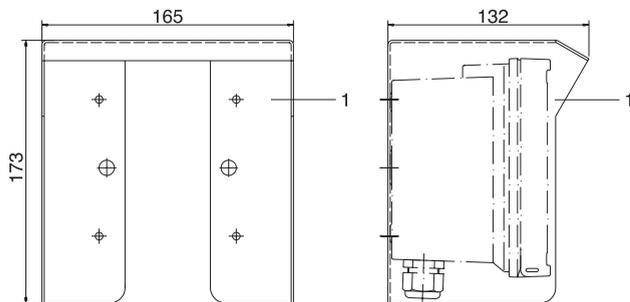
Auvent de protection ZU 0276 pour montage mural et sur poteau
